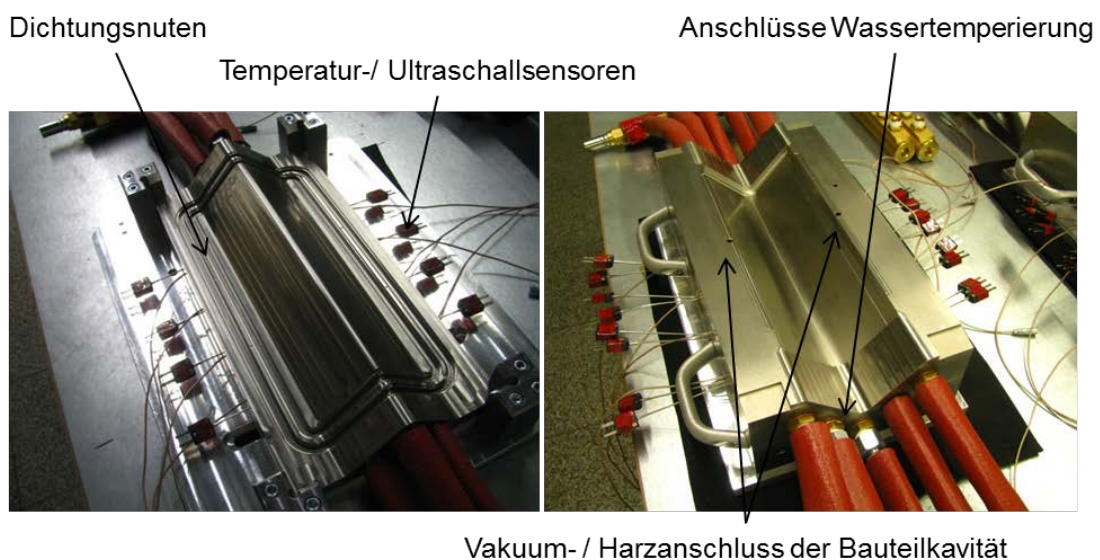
L-Winkelprofil-Werkzeug, RTM Ober- und Unterwerkzeug
